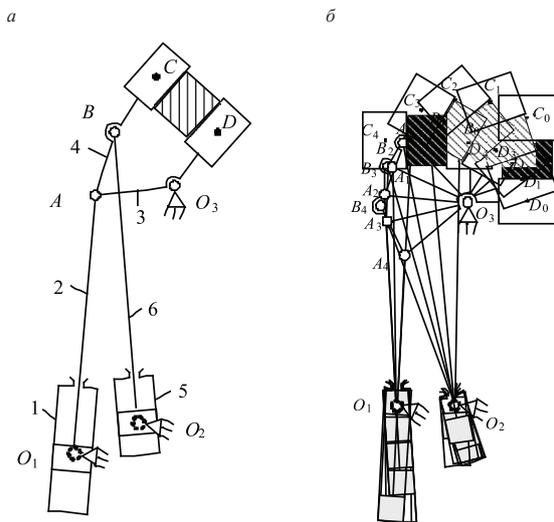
Схема роликового кантователя прокатного стана (а) и построение положений механизма для режима кантовки заготовки (б)
